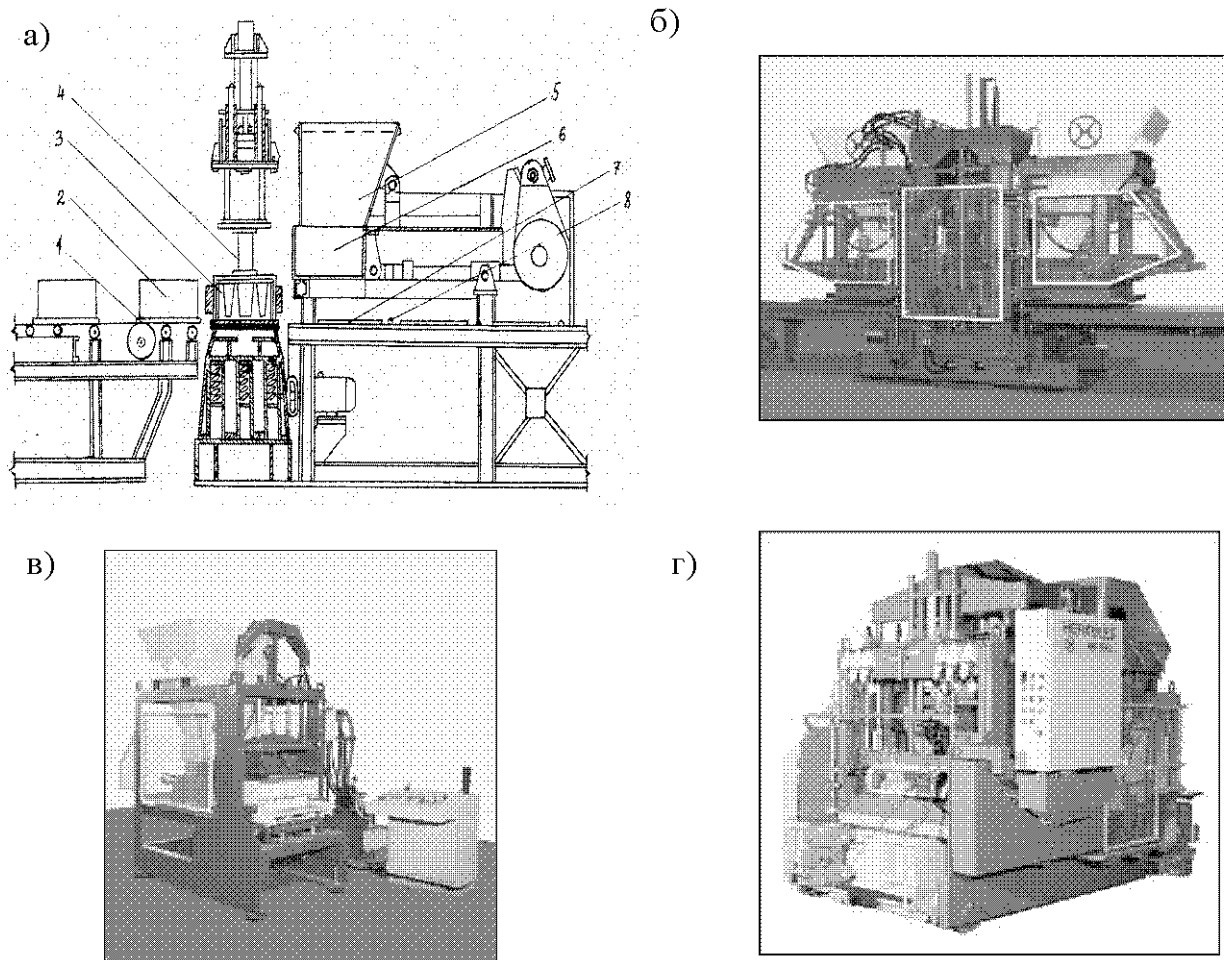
Вібропресове обладнання: а — принципова схема вібропресу; б — двобункерний стаціонарний вібропрес; в — стаціонарний вібропрес; г — пересувний вібропрес; 1 — механізм піднімання виробів; 2 — виріб; 3 — матриця; 4 — пуансон; 5 — бункер; 6 — мірний ящик; 7 — формувальний піддон; 8 — механізм переміщення піддонів.
